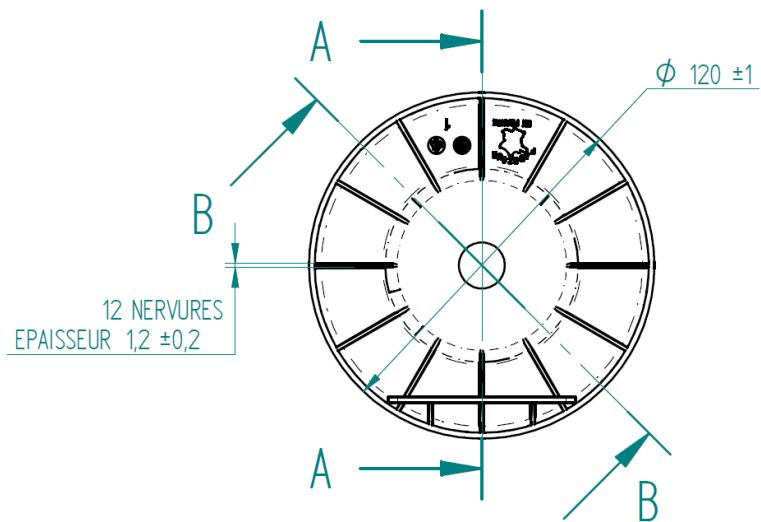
Vis Z103064LAMB, Z103065LAMB ou Z103066LAMB (vue de dessus)
